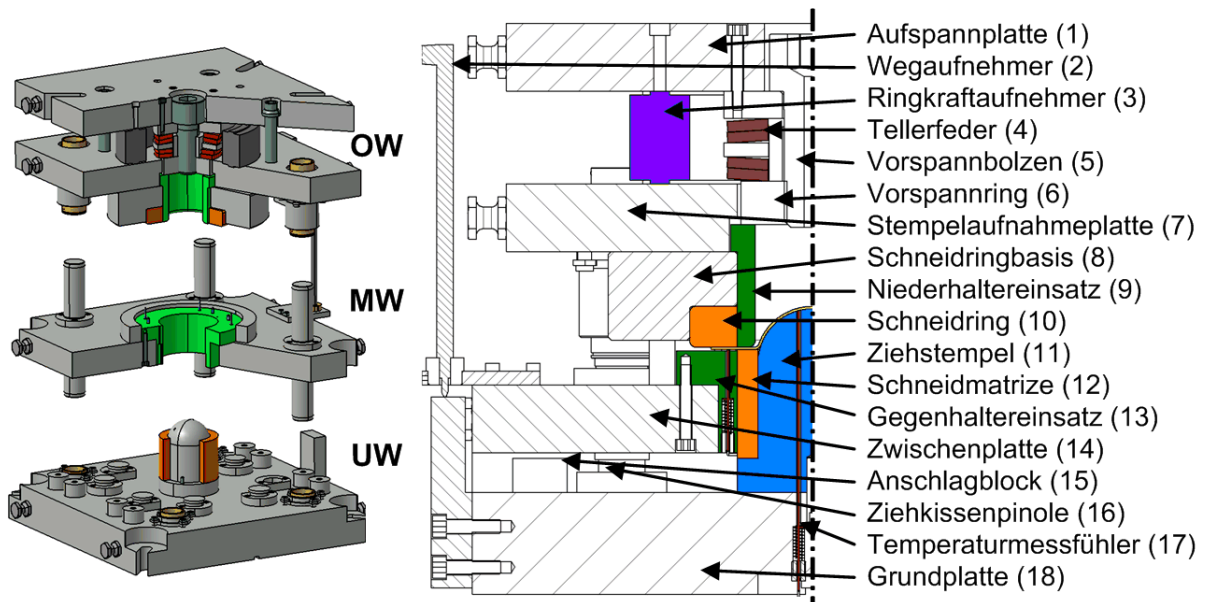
Baugruppen aus dem CAD-Modell und detaillierte Beschreibung der Werkzeugkomponente des aufgebauten Versuchswerkzeugs
